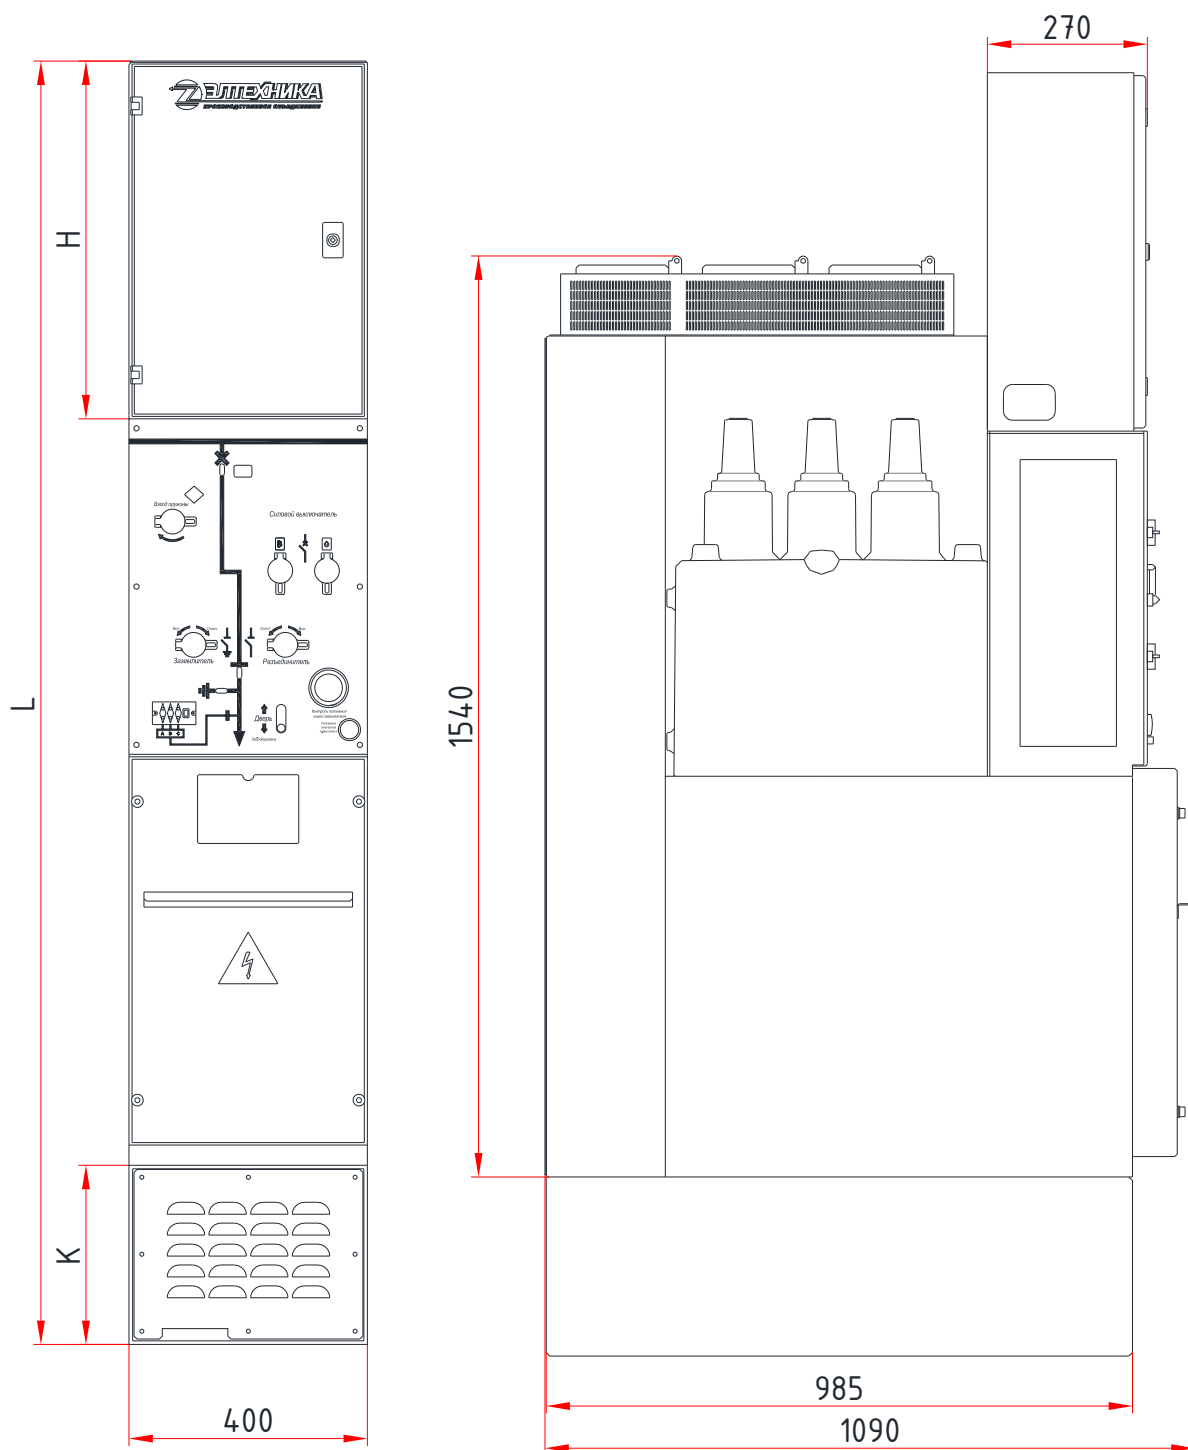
Габаритные размеры шкафов КРУ на номинальный ток 1250А на цоколе
